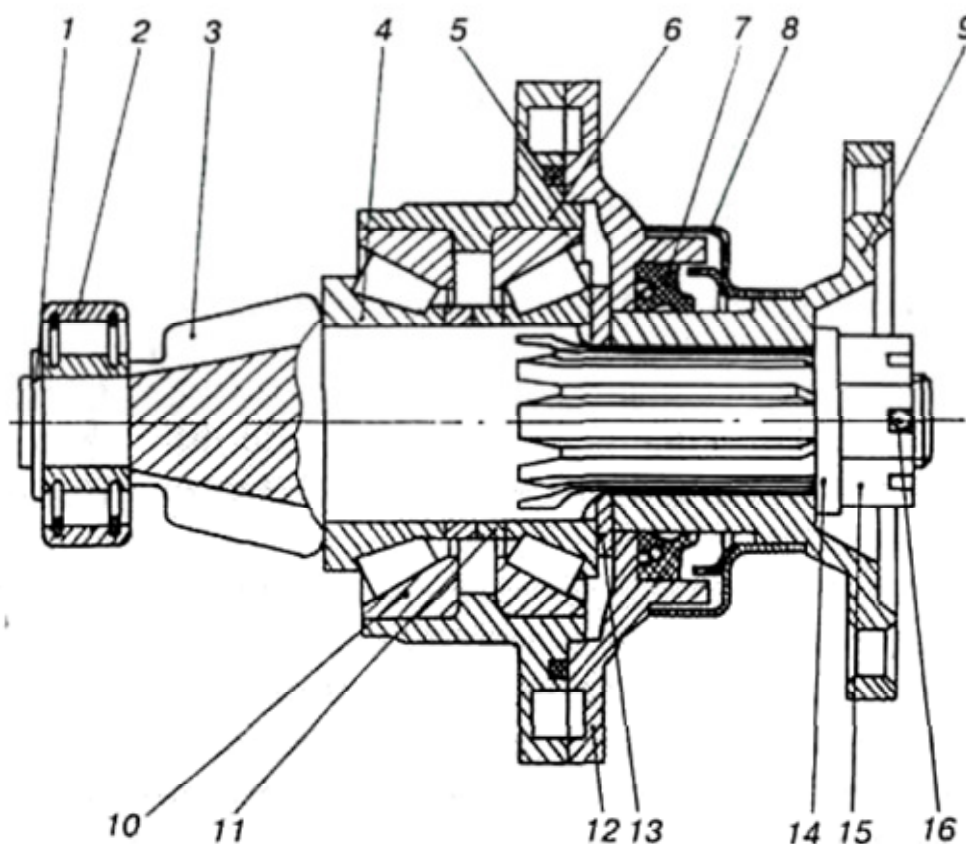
Шестерня ведущая главной передачи заднего мостас картером подшипников: где, 7 — кольцо стопорное; 2 — подшипник роликовый; 3 — вал-шестерня ведущий; 4 — кольцо подшипника внутреннее в сборе с
